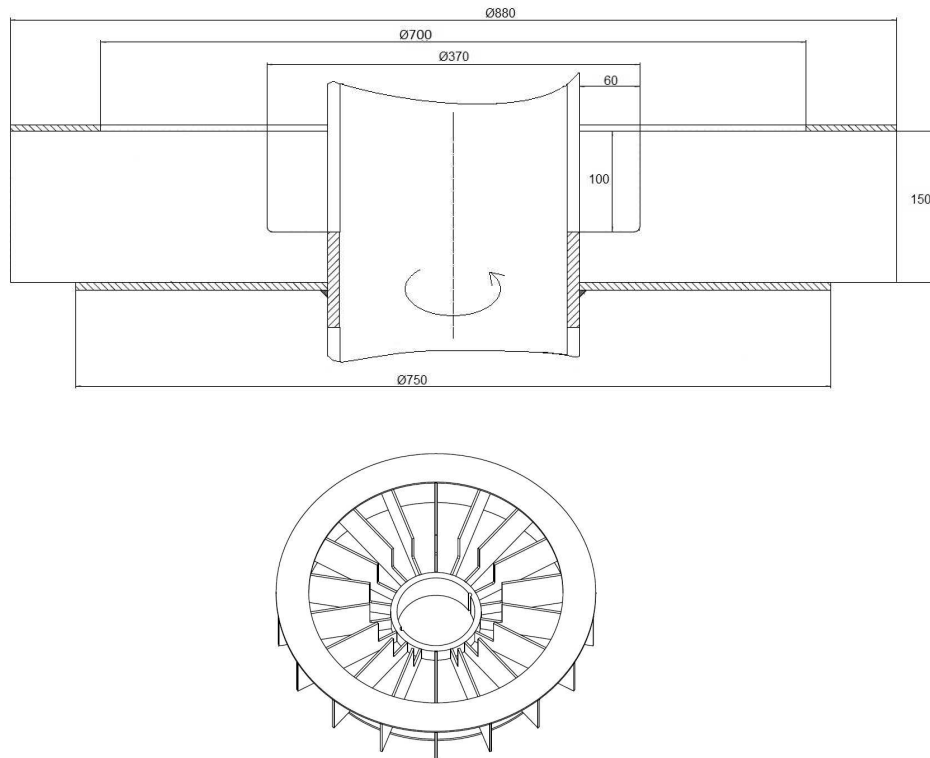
/5: Sichterradgeometrie der GAW Rührwerkskugelmühle: Maßzeichnung und ISO Ansicht [3]
